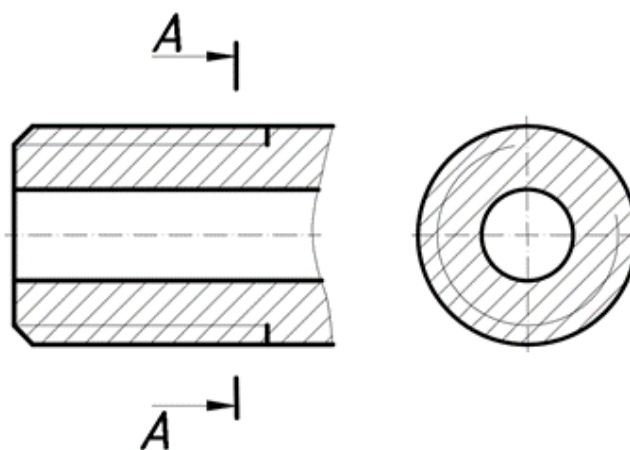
Образец условного изображения наружной резьбы в разрезе
